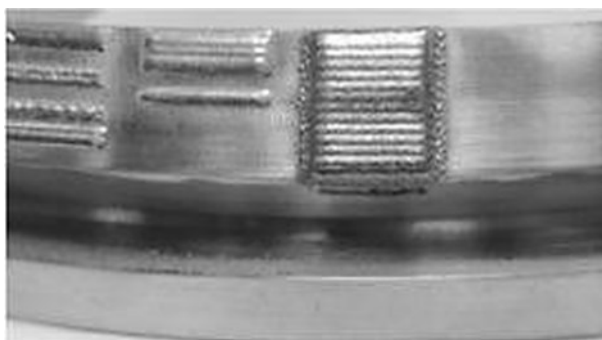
Наплавленные слои на конической поверхности тестовой заготовки
